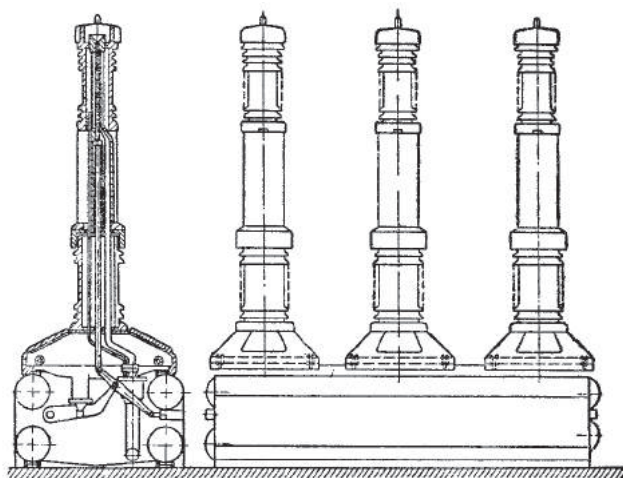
12 Внешний вид и разрез колонкового выключателя с гашением дуги сжатым воздухом фирмы АЭГ с одним разрывом цепи тока на полюс для напряжений 60–200 кВ (1933 г.)
